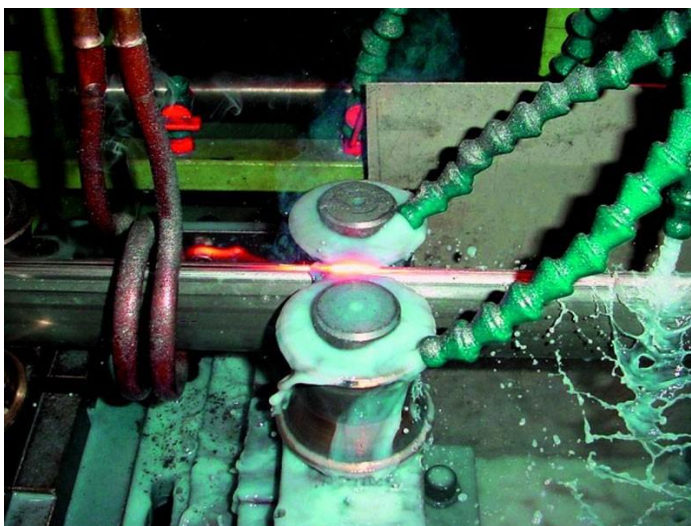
Процесс высокочастотной сварки
